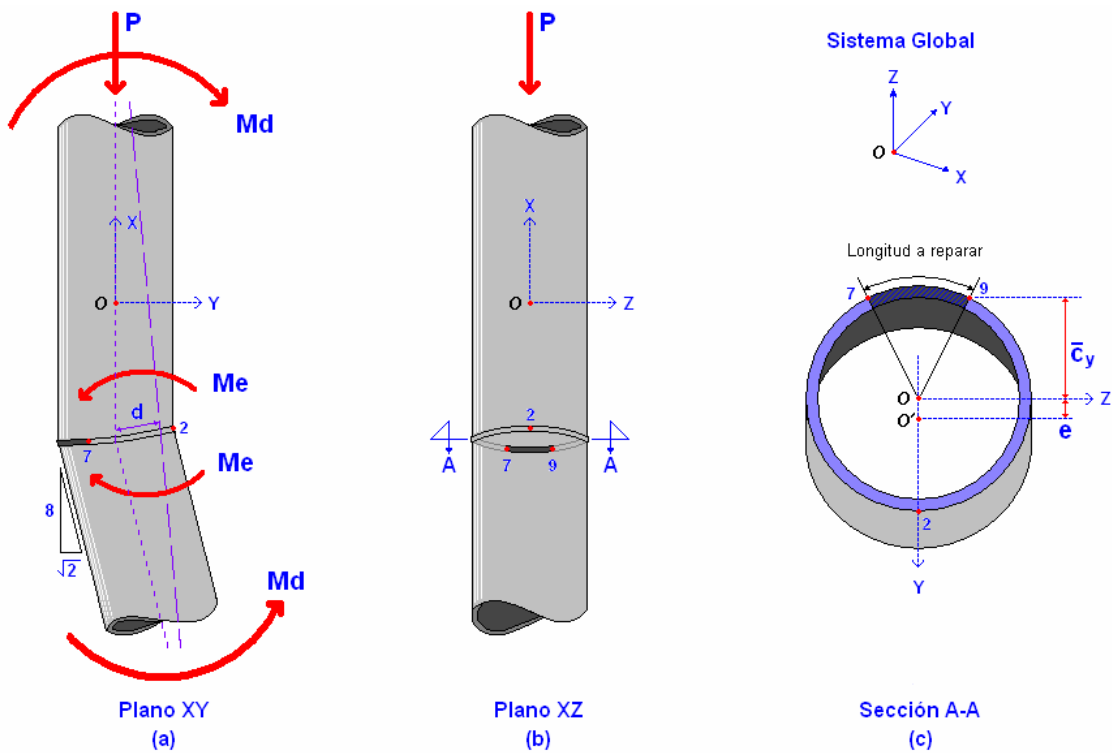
Reparación de soldadura en el cambio de pendiente, en la parte externa.
